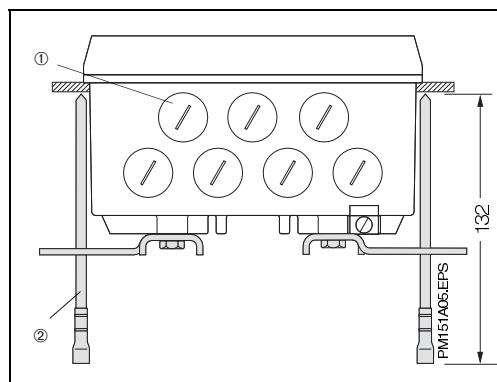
Fond du boîtier de protection avec dimensions et vis de serrage pour un montage en armoire électrique.
